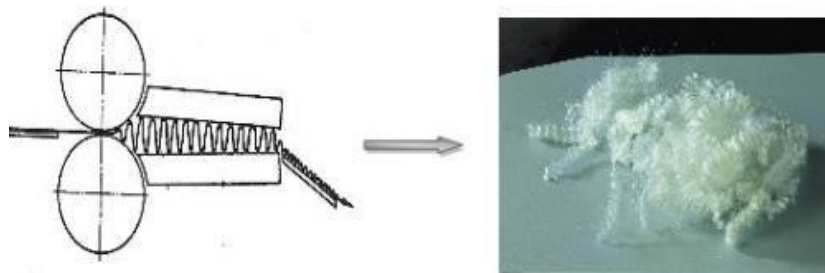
Dispositif de machine de frisage de fibre (Crimper)
